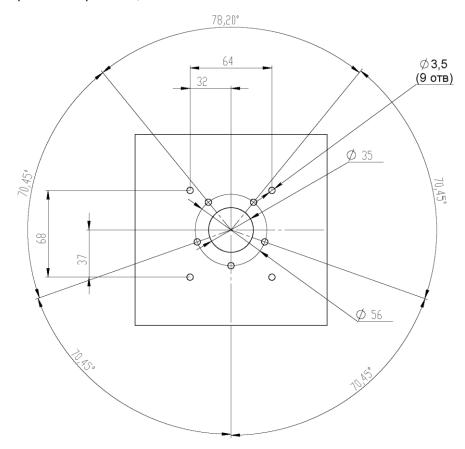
Подготовка топливного бака – крепление с помощью саморезов
